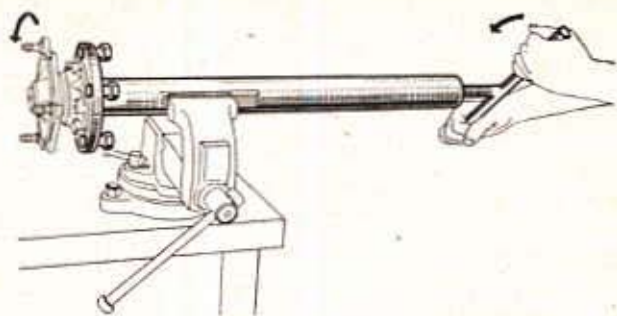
Extraction de l'ensemble : bride - joint d'étanchéité roulement - frette
